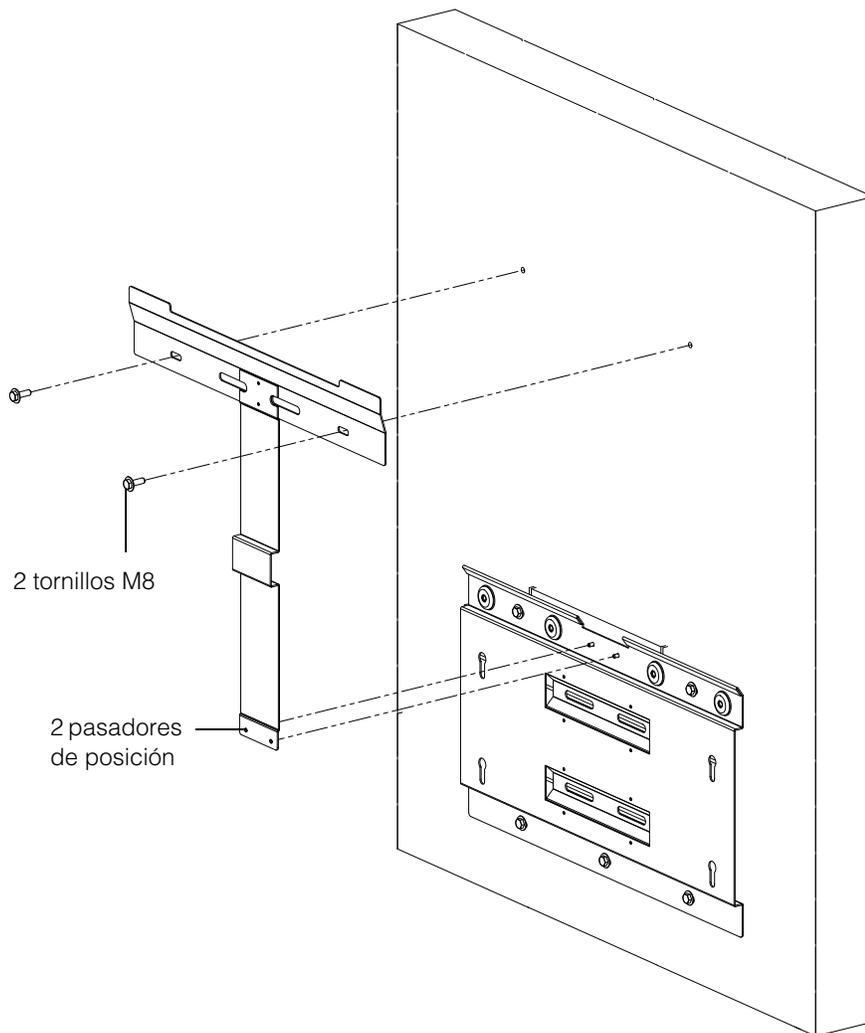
Fijación a la pared de la placa de montaje del inversor
